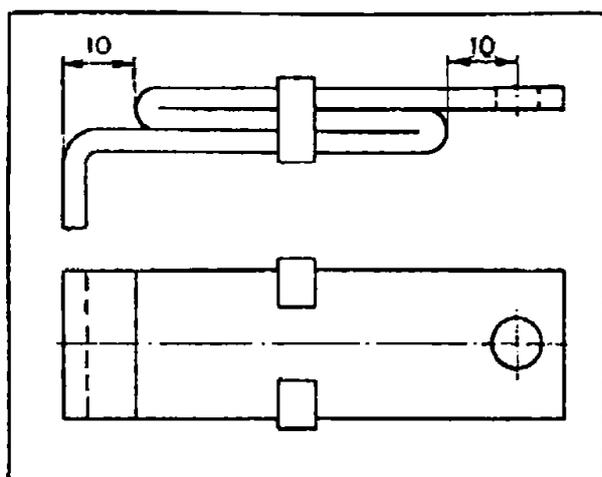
Нагревательный элемент из полосы (с дополнительным изгибом)
